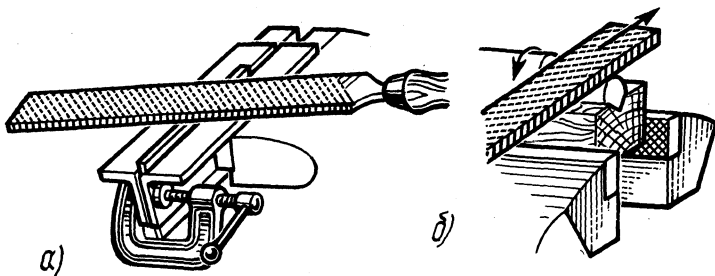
Закрепление для опиливания тонкой заготовки (а) и круглой (б)
